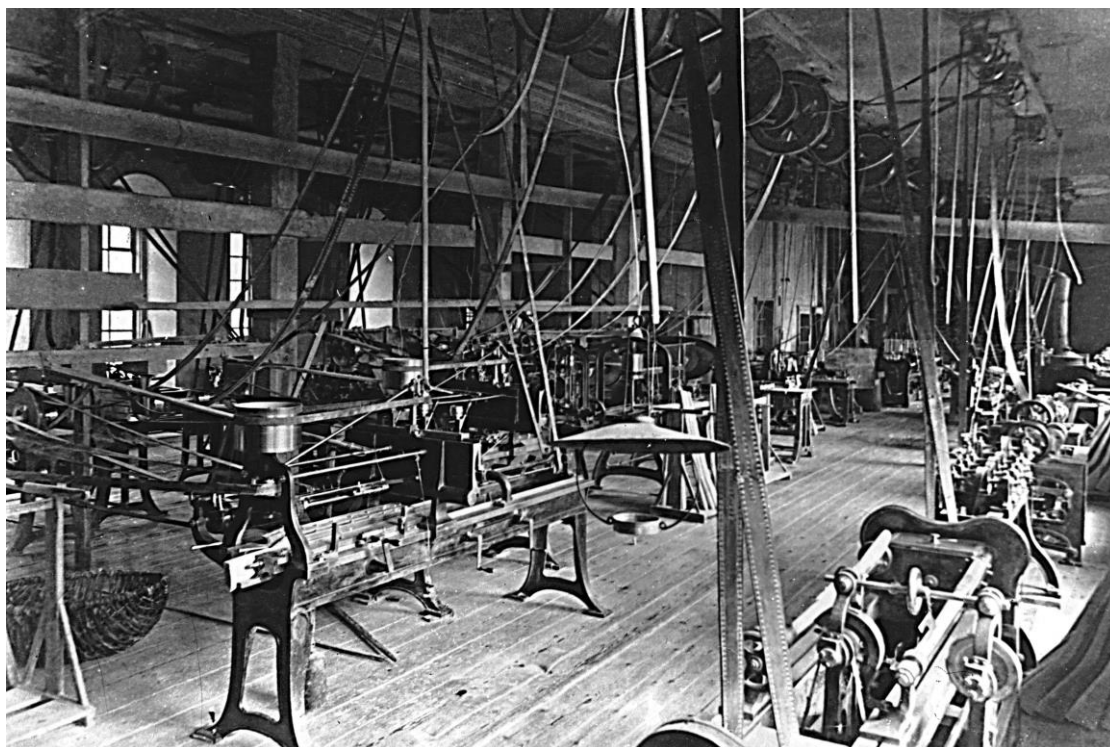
Фото конца 19 века. Ложевая мастерская. Справа копировально-фрезерный станок, слева станок для проточки канала ствола в ложевой болванке [В:8]
